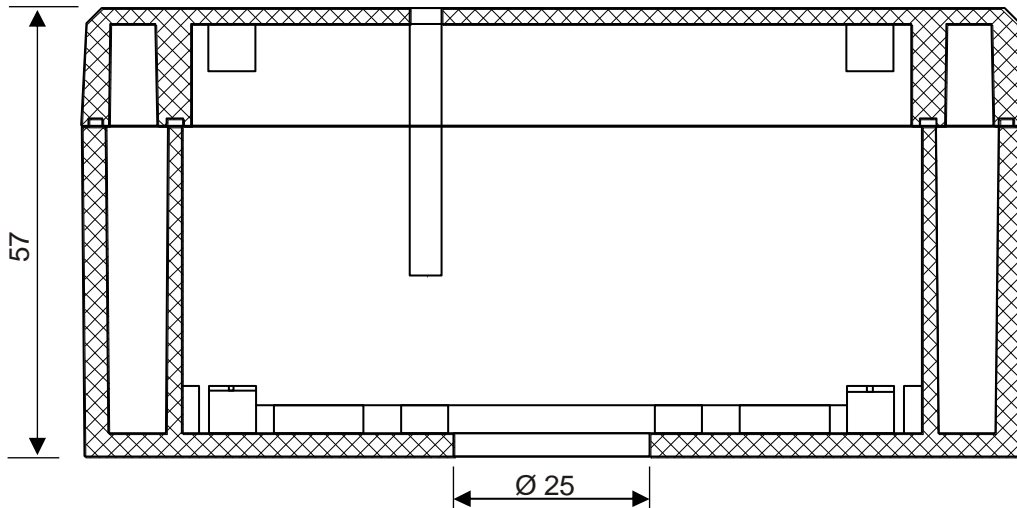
Чертеж радиомодуля VX-RGW с размерами (с крышкой)
